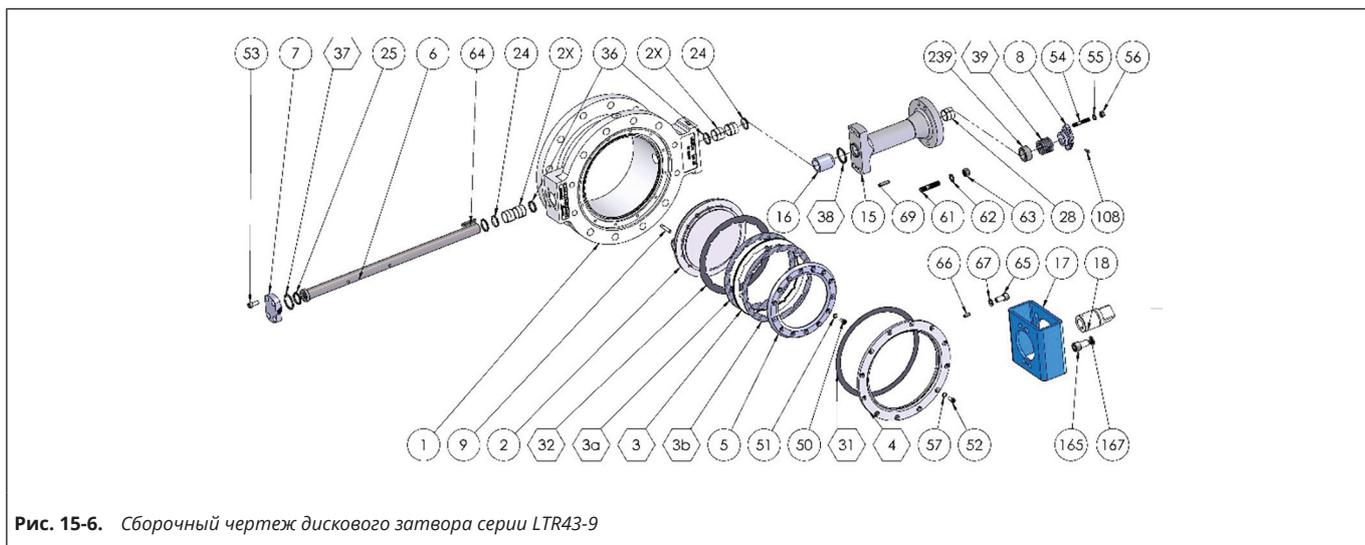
Сборочный чертеж дискового затвора серии LTR43-9
